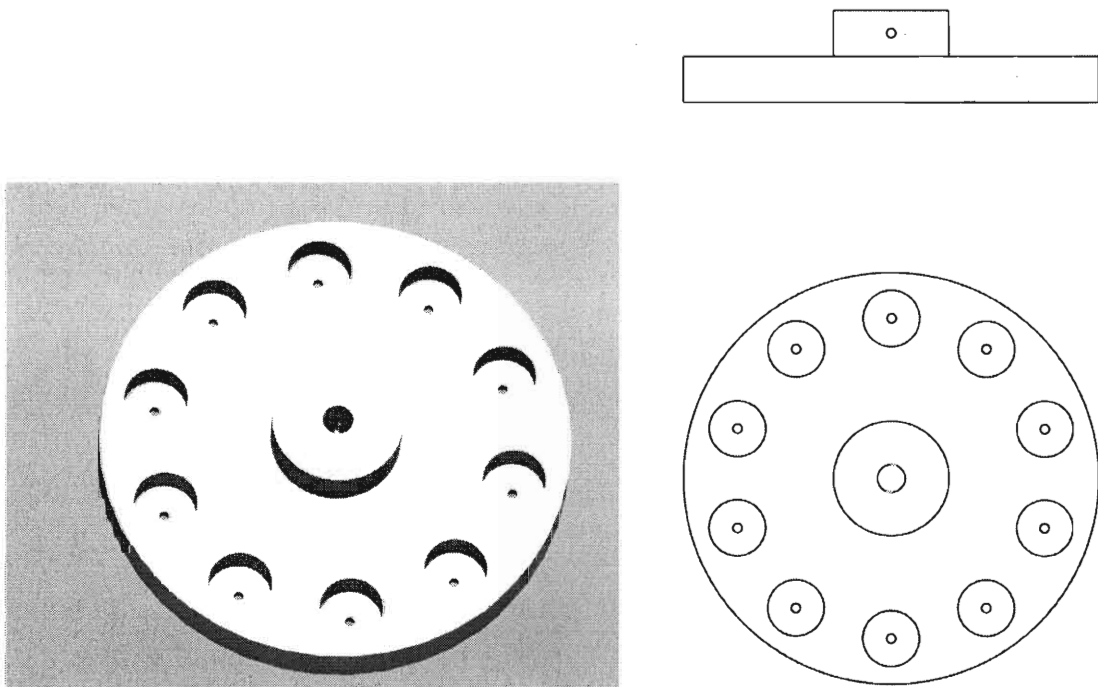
Placa mobilă utilizată ca suport pentru recipientele de colectare a probelor
